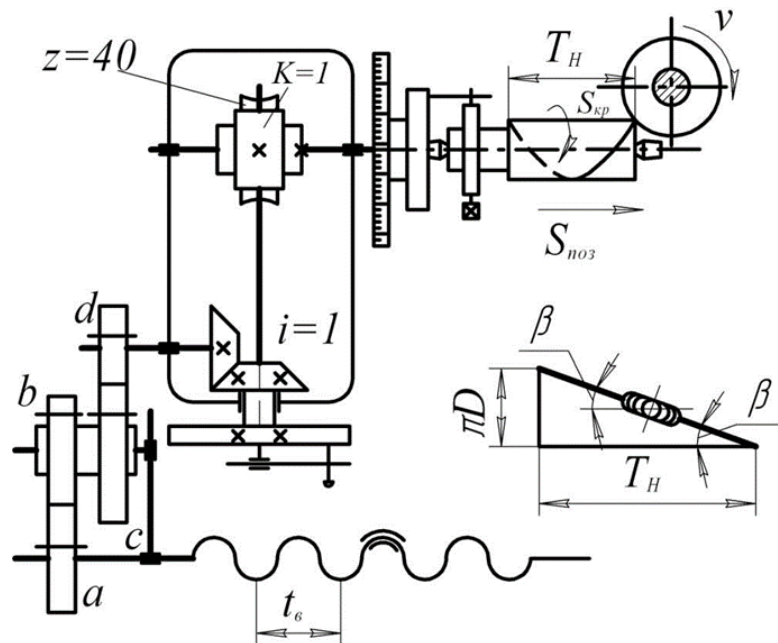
Схема налагодження ділильної головки на фрезерування спіральних канавок
